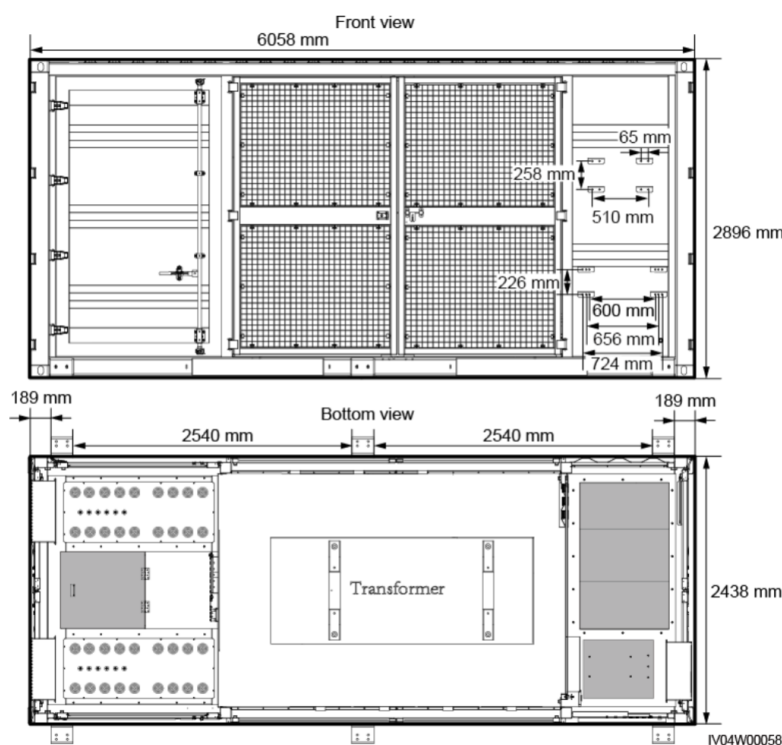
Planimetria e prospetti dell'unità di trasformazione.
